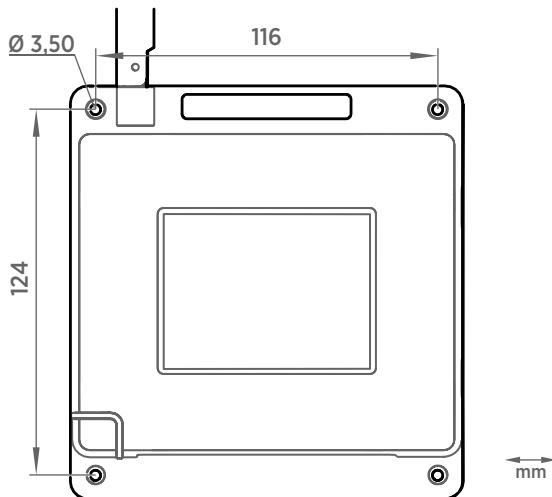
Maße für die Befestigung des AP10 mit Schrauben
